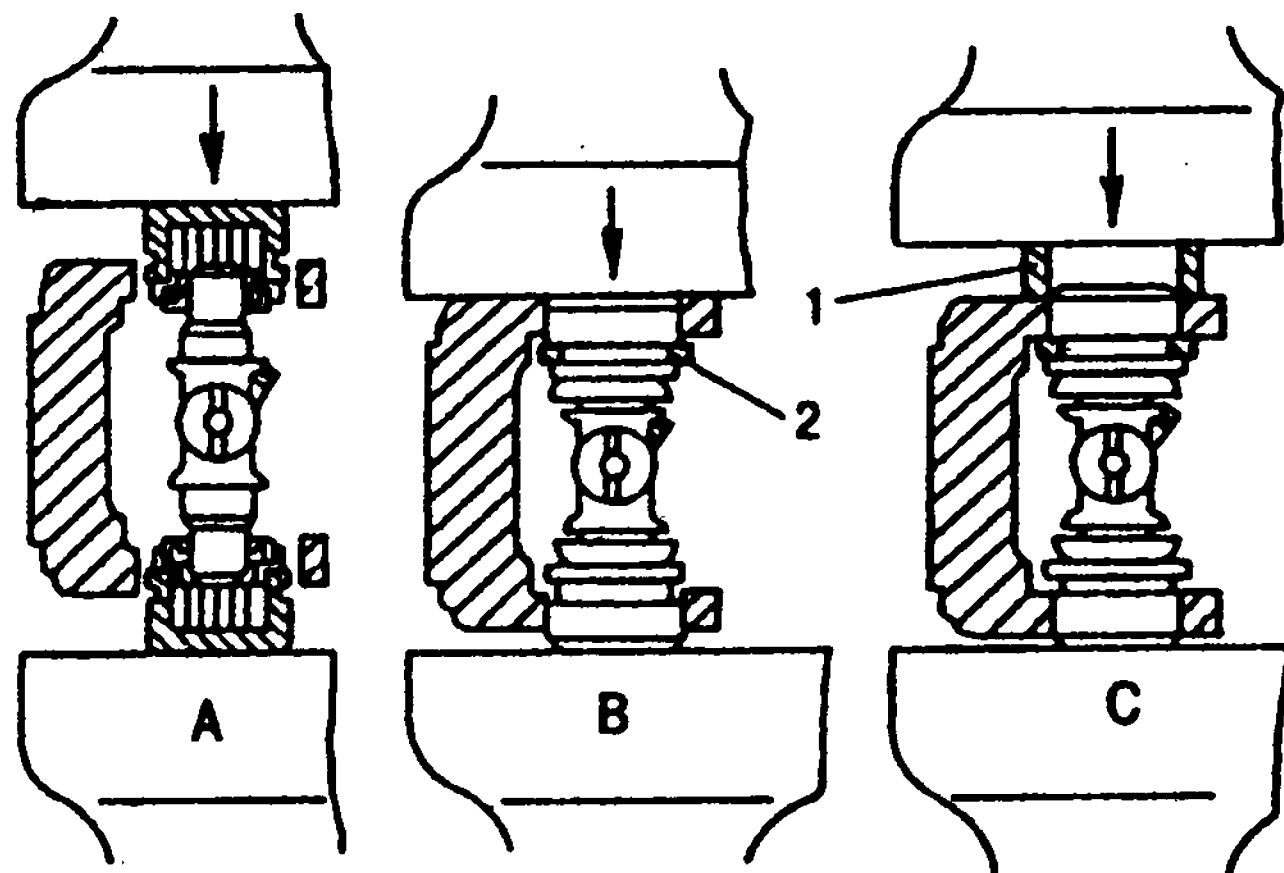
Сборка карданного шарнира; 1 - кольцо; 2 - стопорное кольцо
